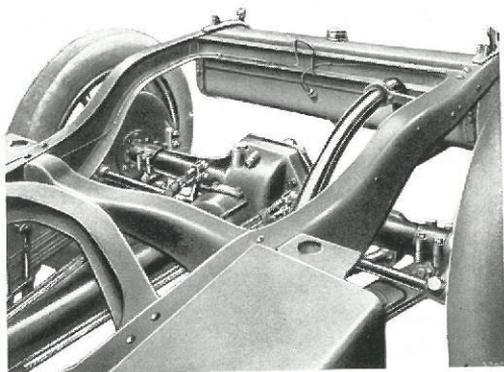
Tuyau d'échappement et attaches de la carrosserie
